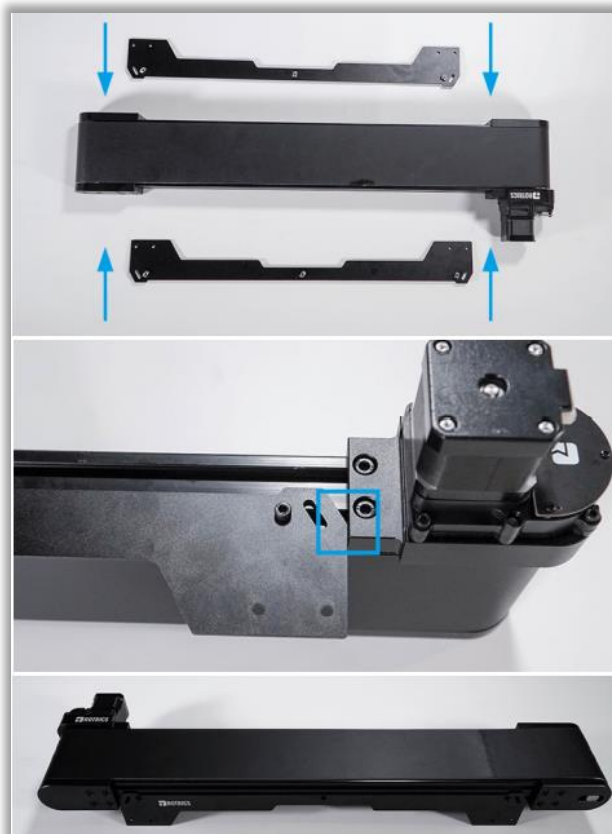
Сборка верхней части конвейерной ленты
